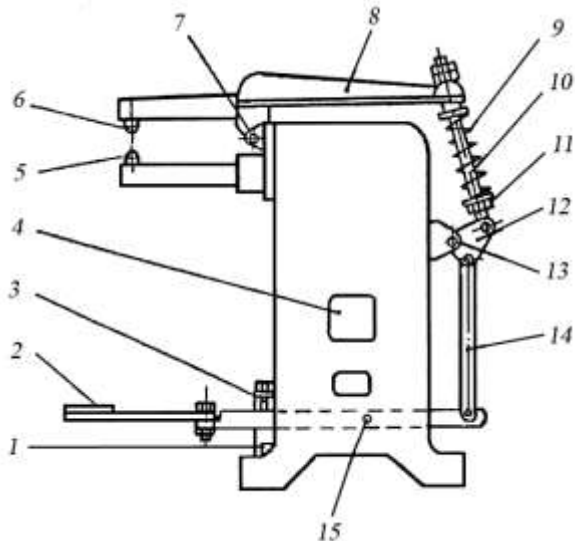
Машина АТП - 10 для точкового електроконтактного зварювання: 1, 3 - упор; 2 - педаль; 4 - кожух захисний; 5 - електрод нижній; 6 - електрод верхній; 7, 13, 15 - вісь; 8 - важіль; 9 - пружина; 10 - шток верхній; 11 - гайка; 12 - сектор; 14 - шток нижній
